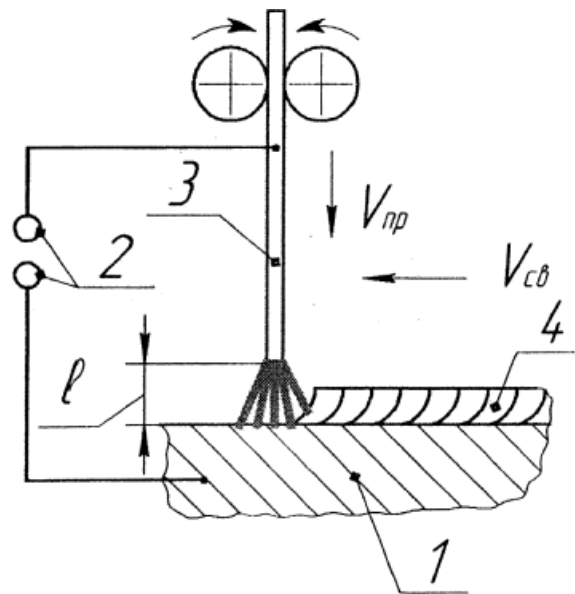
Схема механизированной электродуговой сварки: 1- свариваемое изделие; 2-источник сварочного тока; 3- электродная проволока; 4- сварной шов;  $V_{пр}$ - скорость подачи электродной проволоки, м/ч;  $V_{св}$ - скорость сварки, м/ч;  $l$ - длина сварочной дуги, мм.
